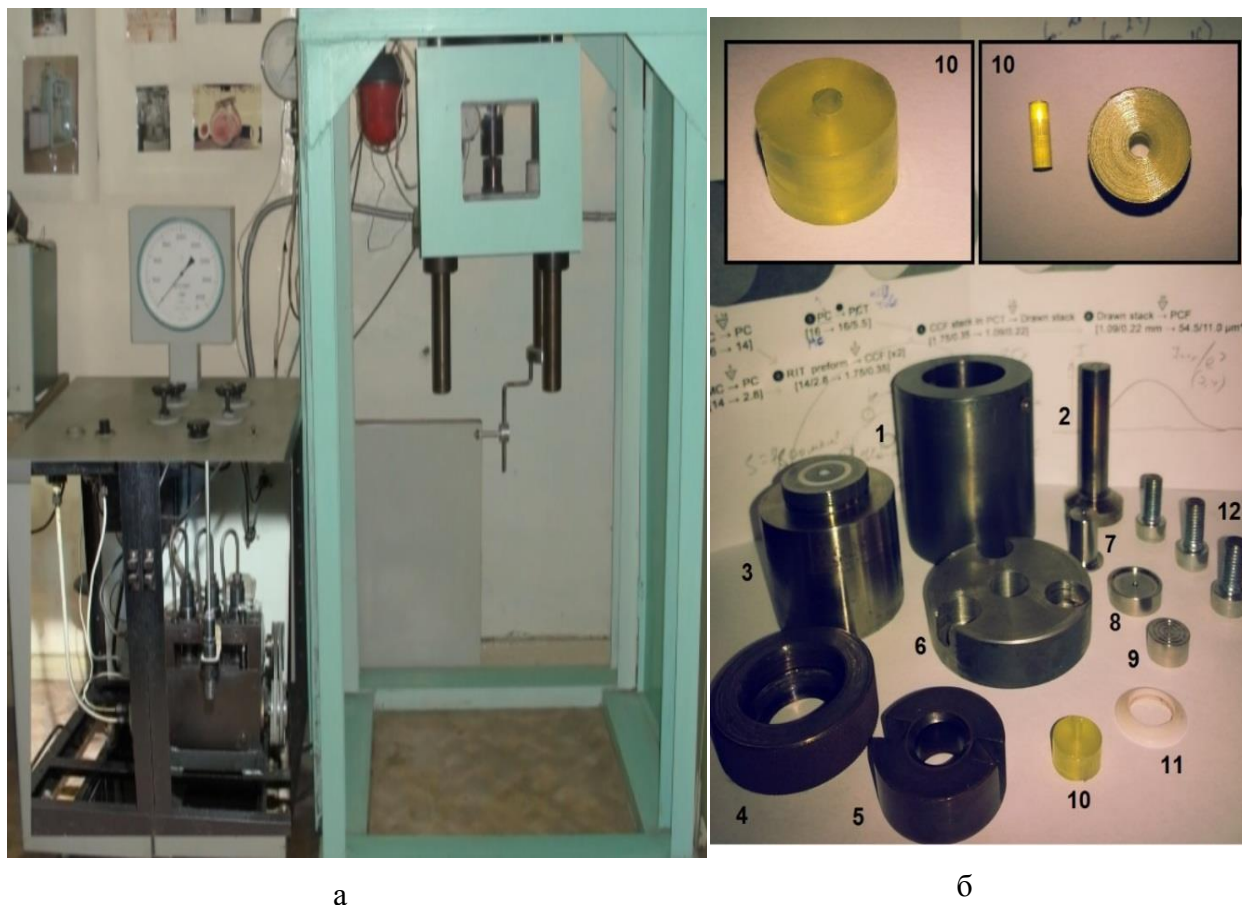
Общий вид пресса ПОИ-500 (а) и оснастки для прессования (б):
